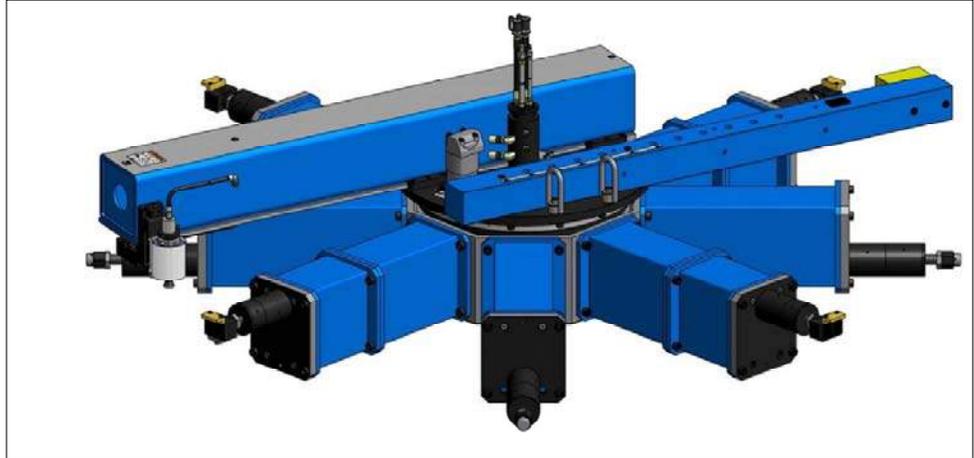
MONTAJE DE REVESTIMIENTO DE BRIDA ID CON CABEZAL MOLEDOR
